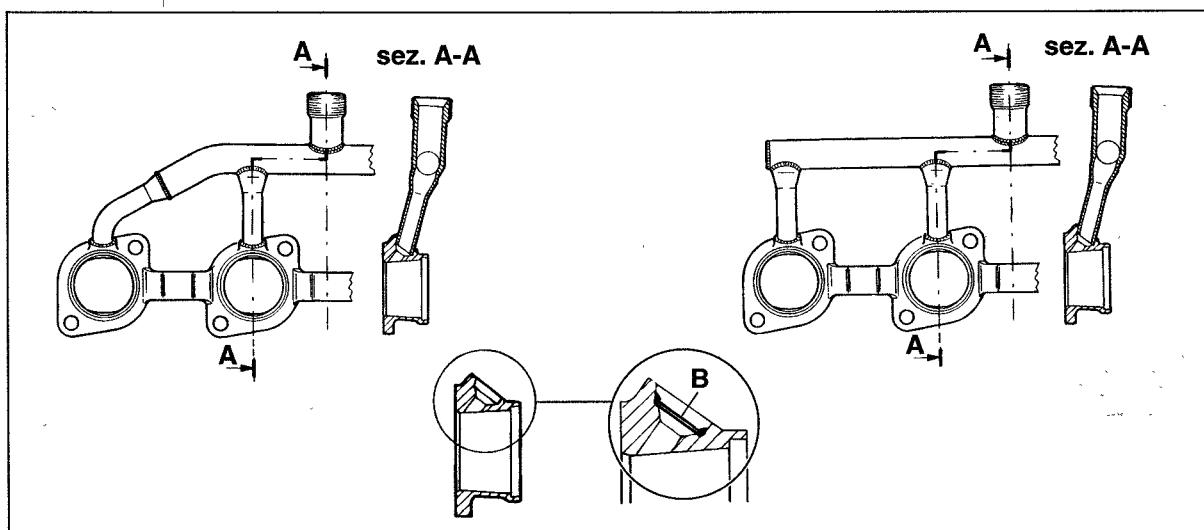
Rimozione tubetti iniezione aria nei collettori di scarico
